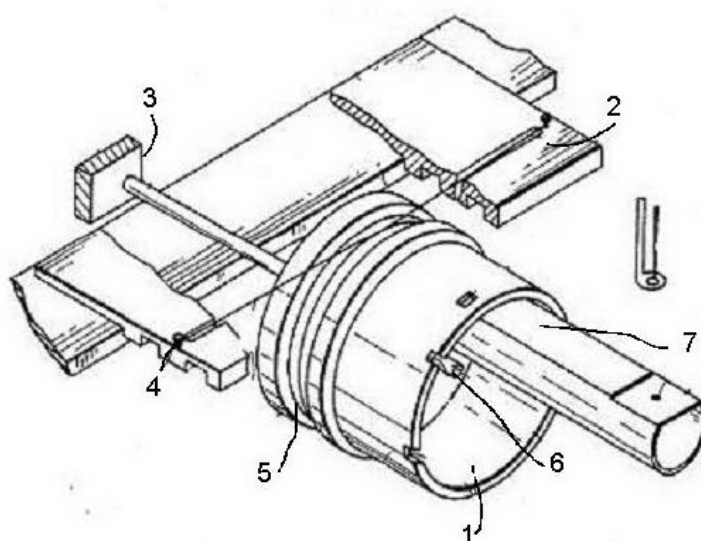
Приспособление для вышивания на готовых изделиях
